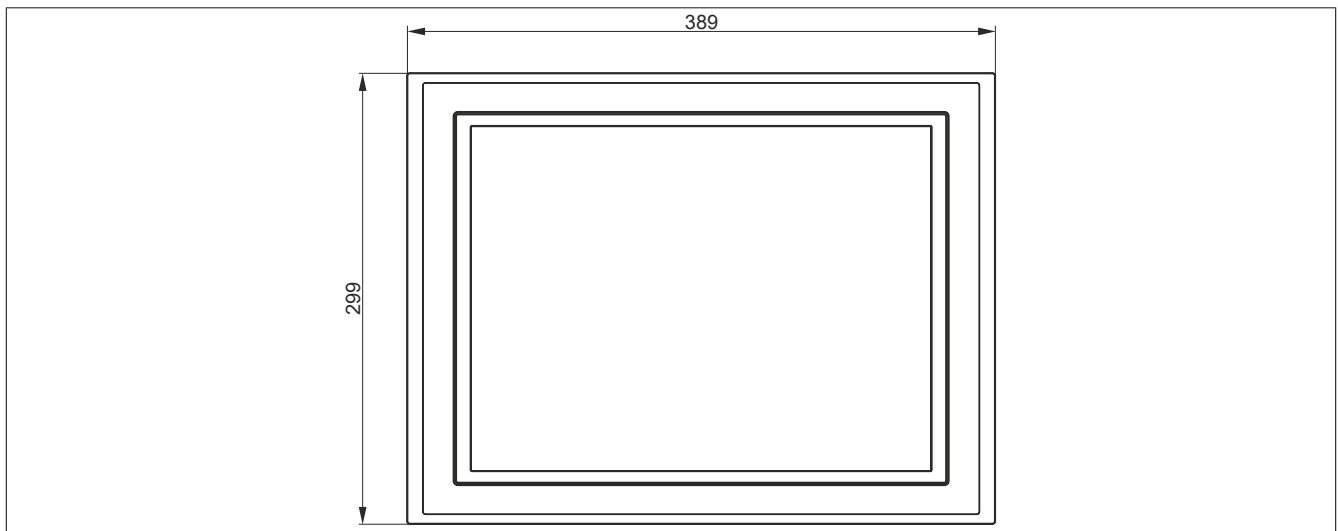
5AP5120.1505-000 - Abmessungen
